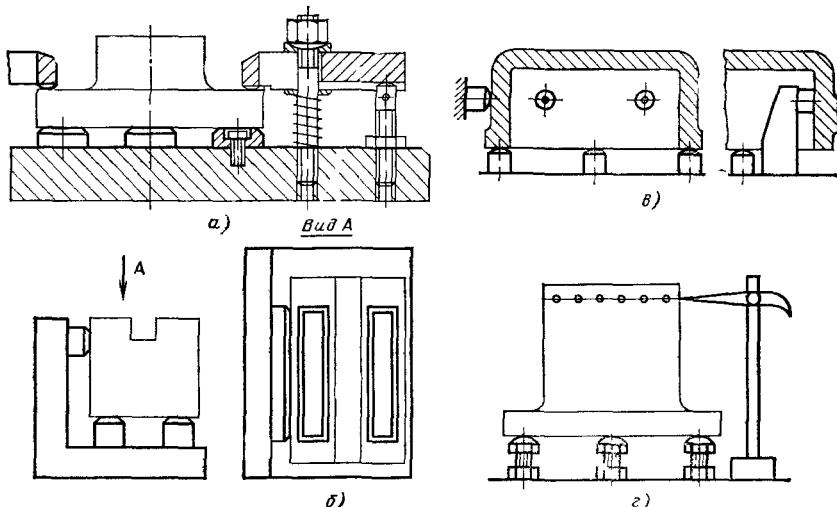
Схемы установки заготовок плоскими по: а — опорные шайбы; б — опорные пластины; в — опорные штири, г — винтовые регулируемые опоры
